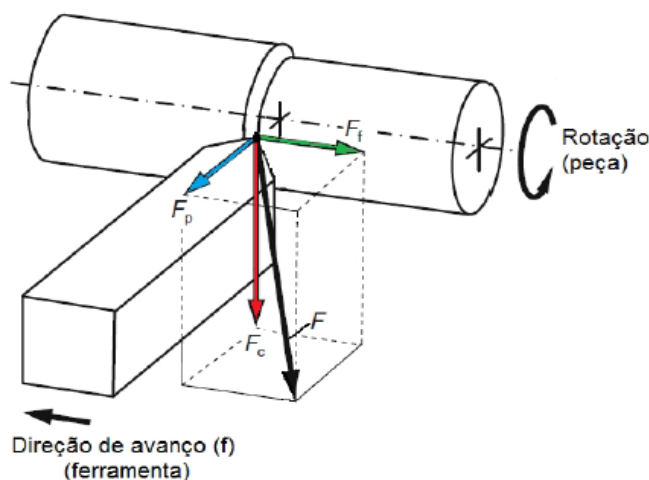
Componentes da força de usinagem [adaptado de Machado *et al.*, 2011].
